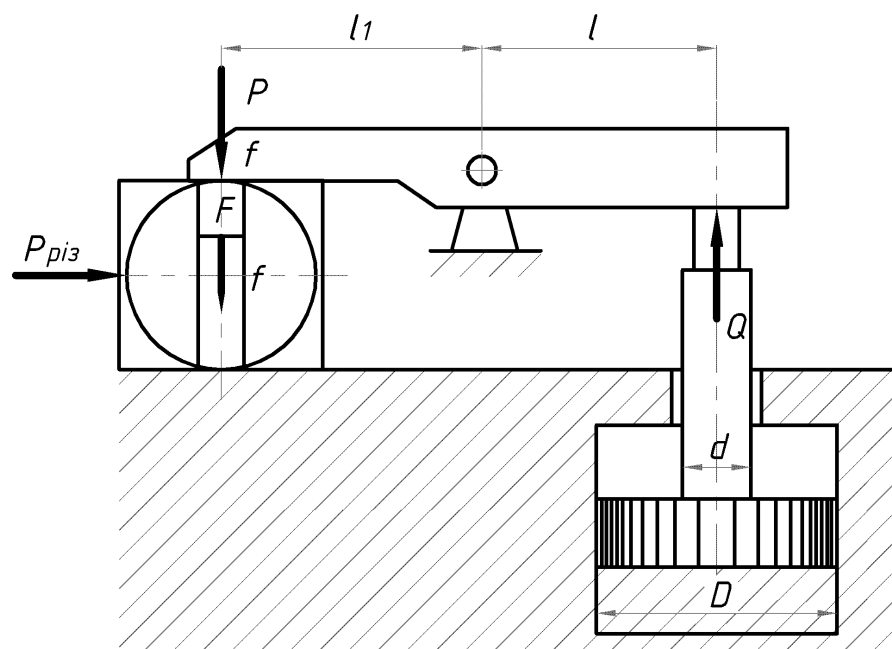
Схема базування та затиску деталі в пристрої для фрезеруванні торців
